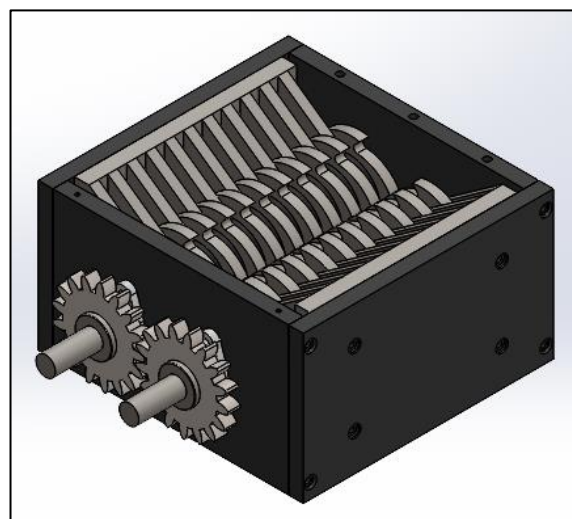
Vista isométrica del ensamblaje final de la cámara de trituración en SolidWorks
